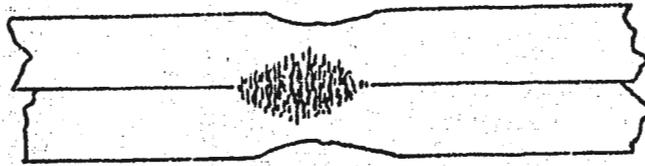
SECCION TRANSVERSAL DE UN PUNTO DE SOLDADURA
